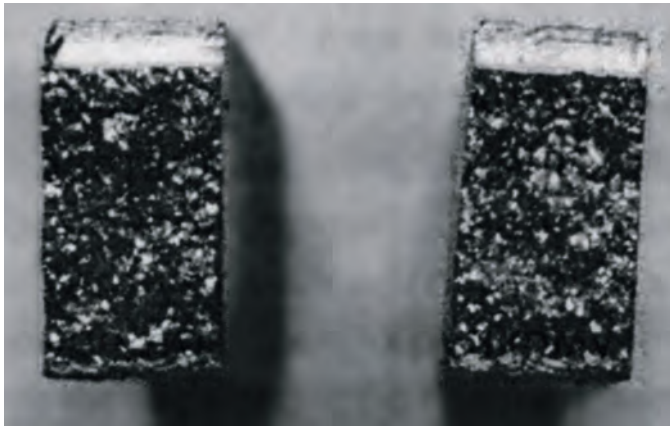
Хрупкий излом образца в месте пережога в сварном соединении
